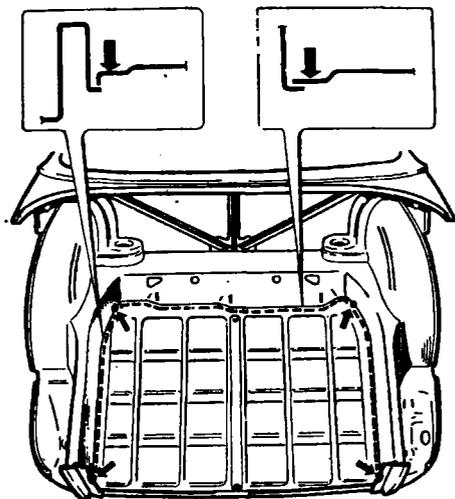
Замена пола задка. Пунктиром обозначены линии рубки, на фрагментах стрелками - места рубки. На основном виде стрелками показаны места газовой сварки
